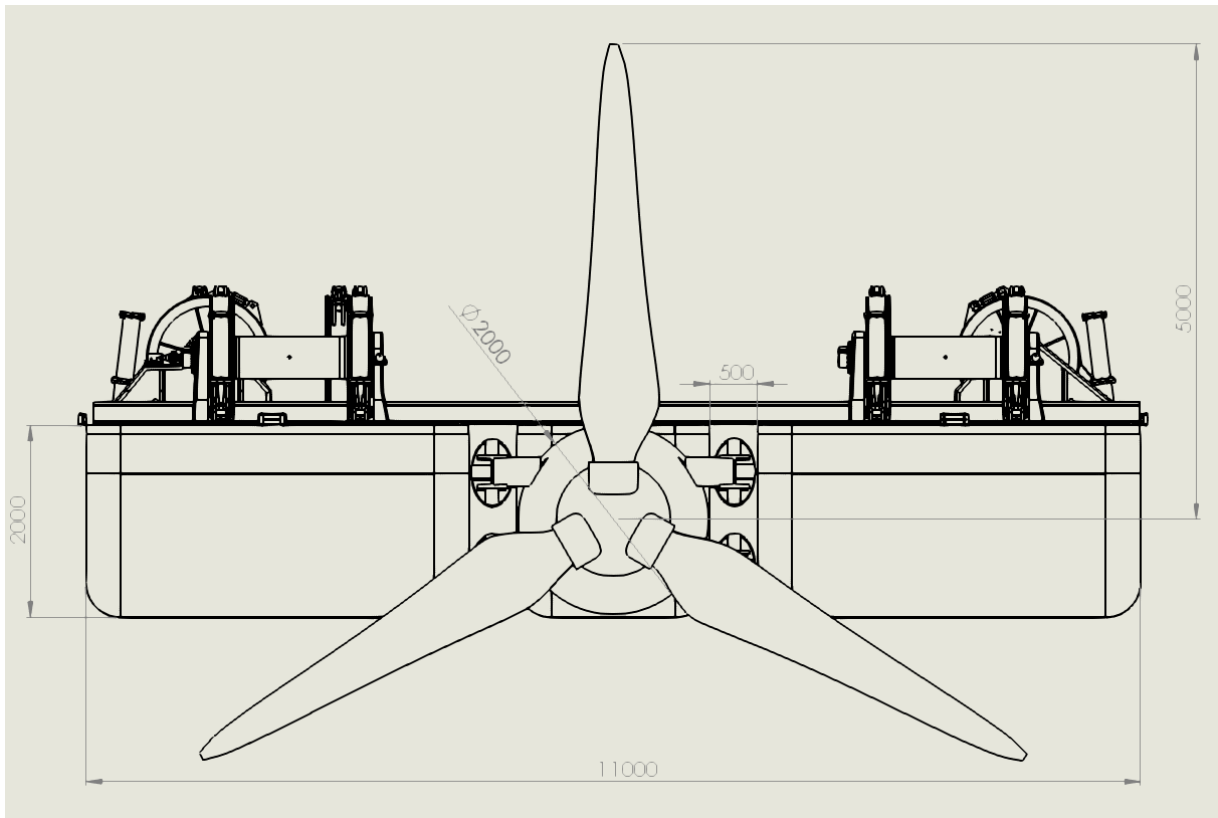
Visão frontal do sistema em manutenção com dimensões em [mm].
